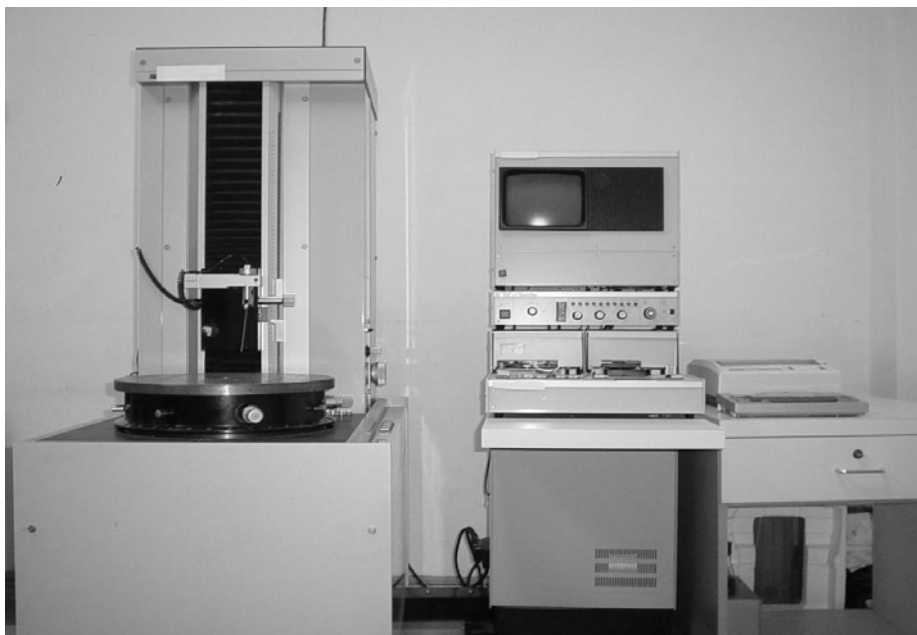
Общий вид установки для измерений геометрических параметров профиля поверхности
